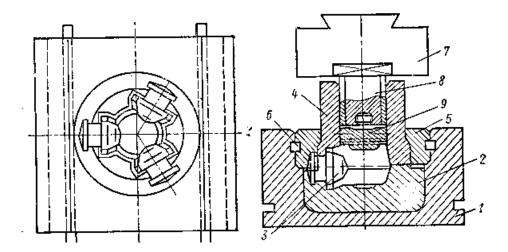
Схема штампа для поперечного выдавливания втулки на гидравлическом прессе 1 – корпус; 2 – вставка; 3 – боковой пуансон; 4 – верхняя часть матрицы; 5 – прижимная плита; 6 – клин; 7 – пуансонодержатель; 8 – державка; 9 – пуансон
